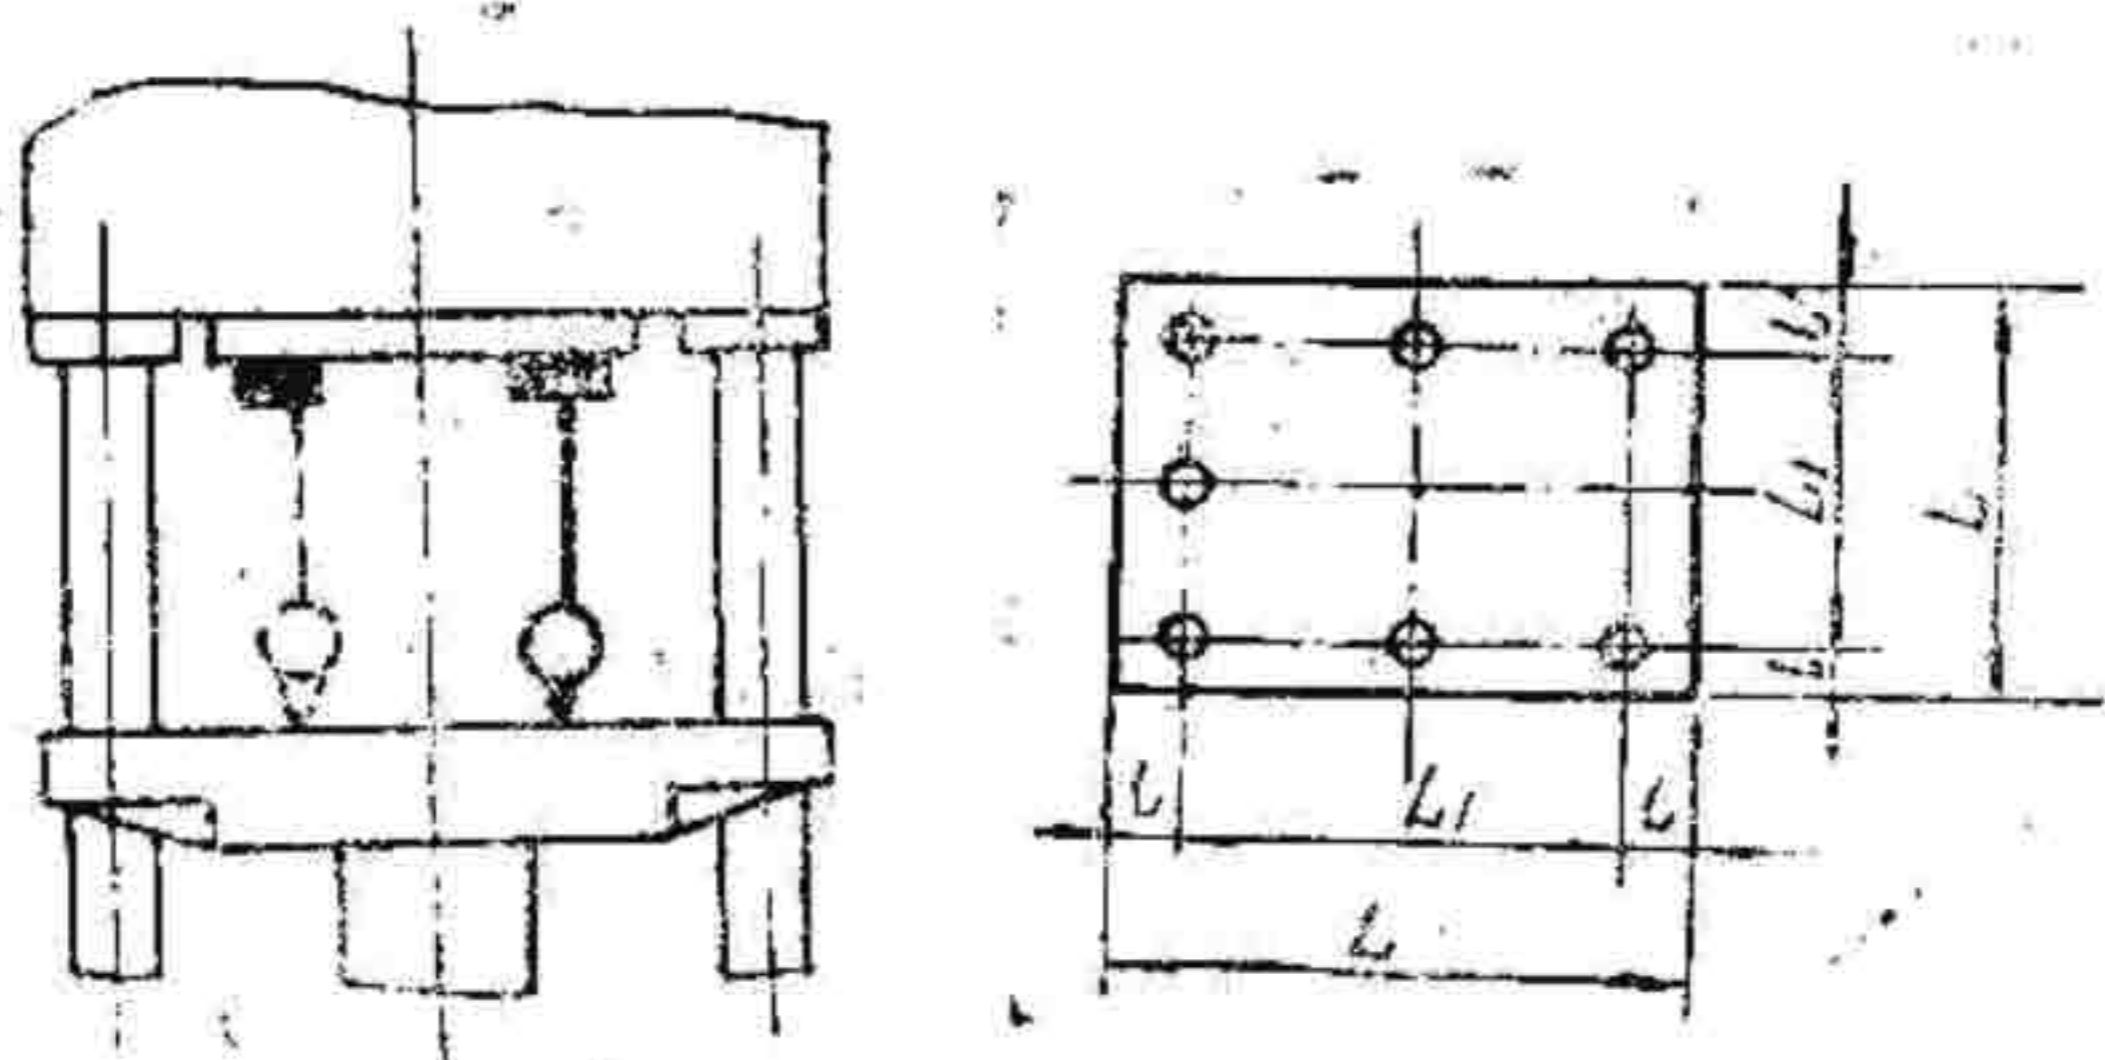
检验活动横梁(滑块)下平面与工作台上平面的平行度
